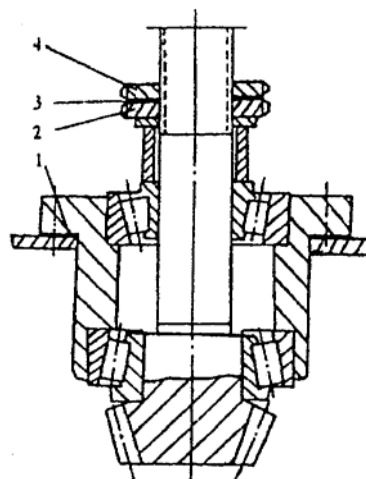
Регулировка предварительного натяга шестерни главной передачи в сборе
